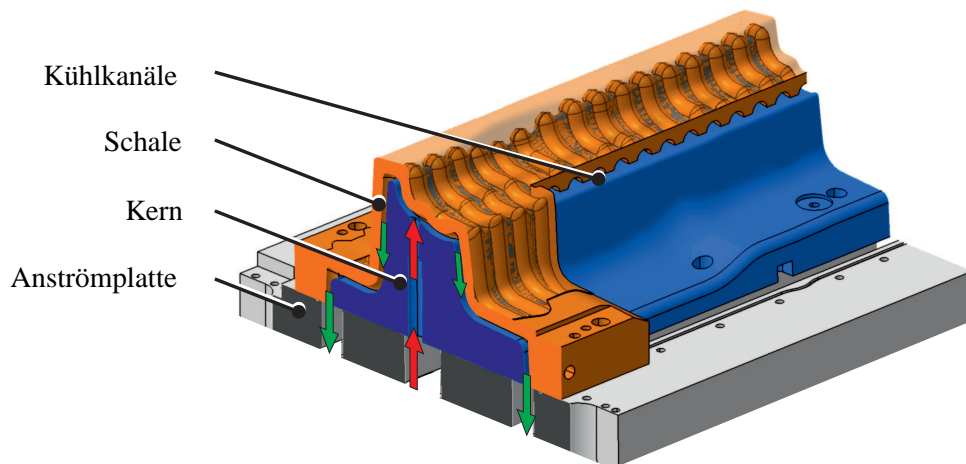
Ausschnitt aus einem Warmformwerkzeug mit gefrästen Kühlkanälen (Schalenkühlung);
